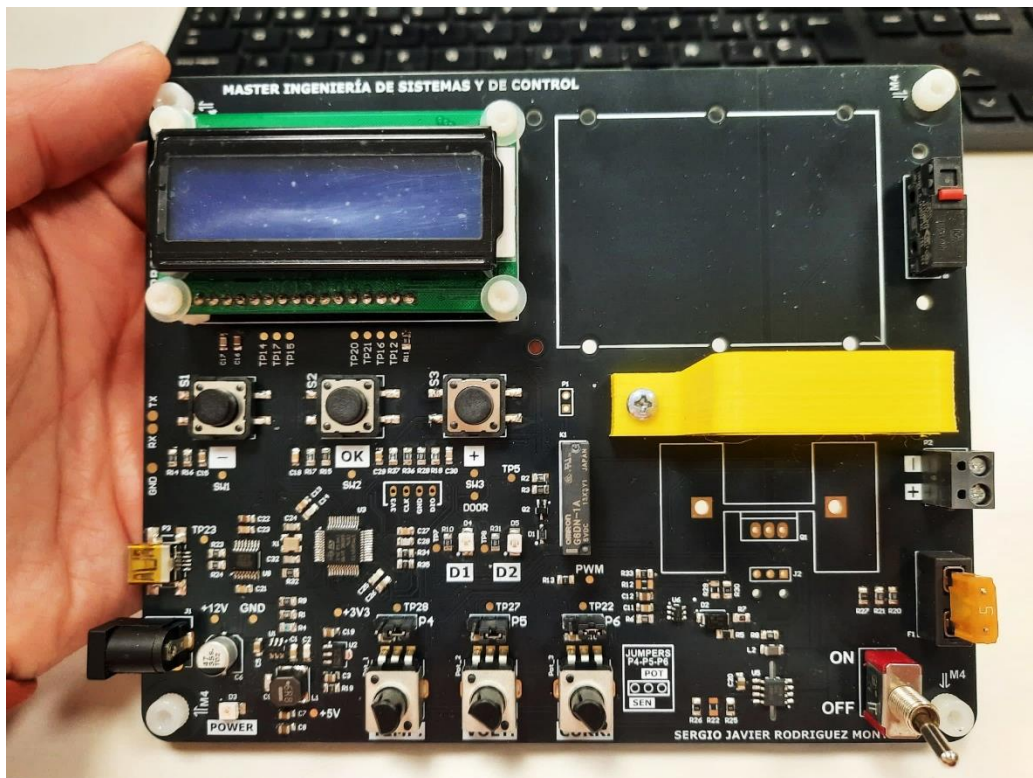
PCB casi ensamblada a falta de algunos componentes grandes y piezas 3D.
